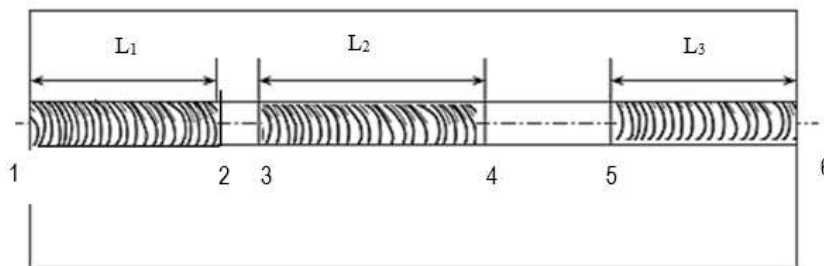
Soldadura a tope con bisel, con seis extremos en el cordón.
